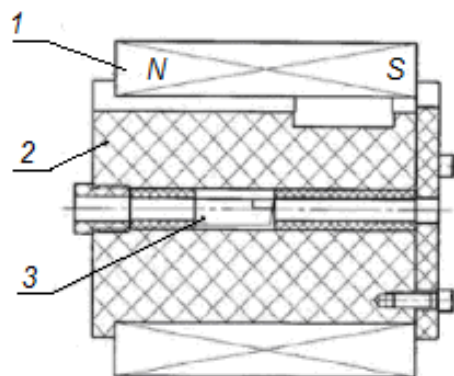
Схема магнітно-імпульсного пластичного поверхневого деформування: 1 – індуктор; 2 – оправка для установки заготівлі, 3 – заготівля
